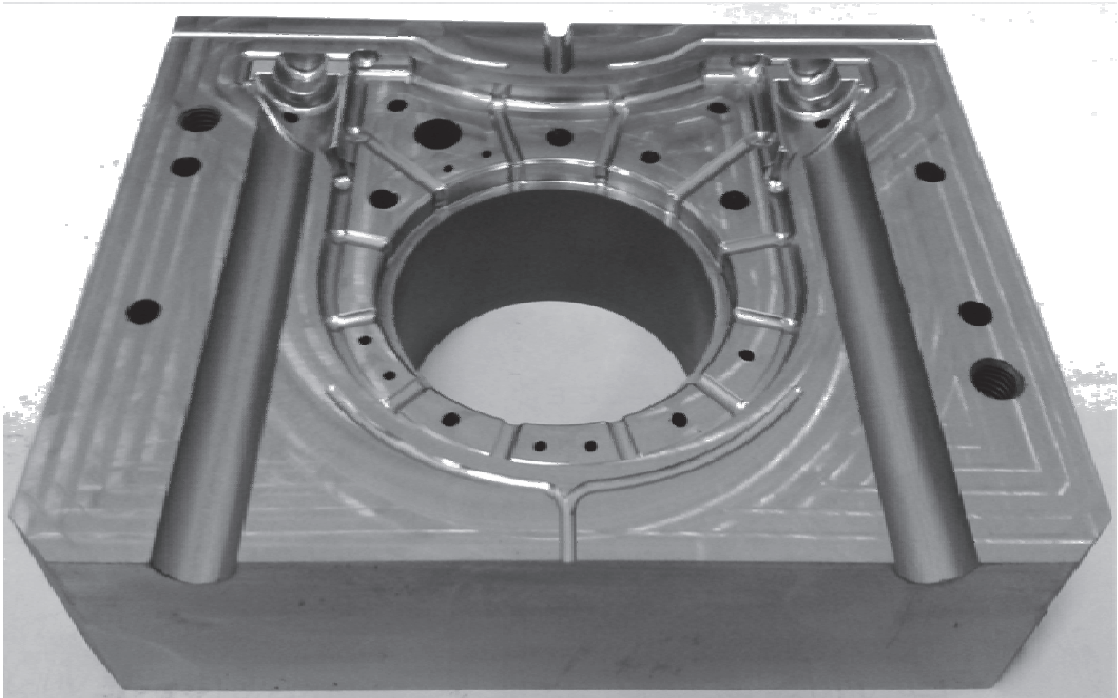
Dráhy nástrojů při frézování tvárníku.
